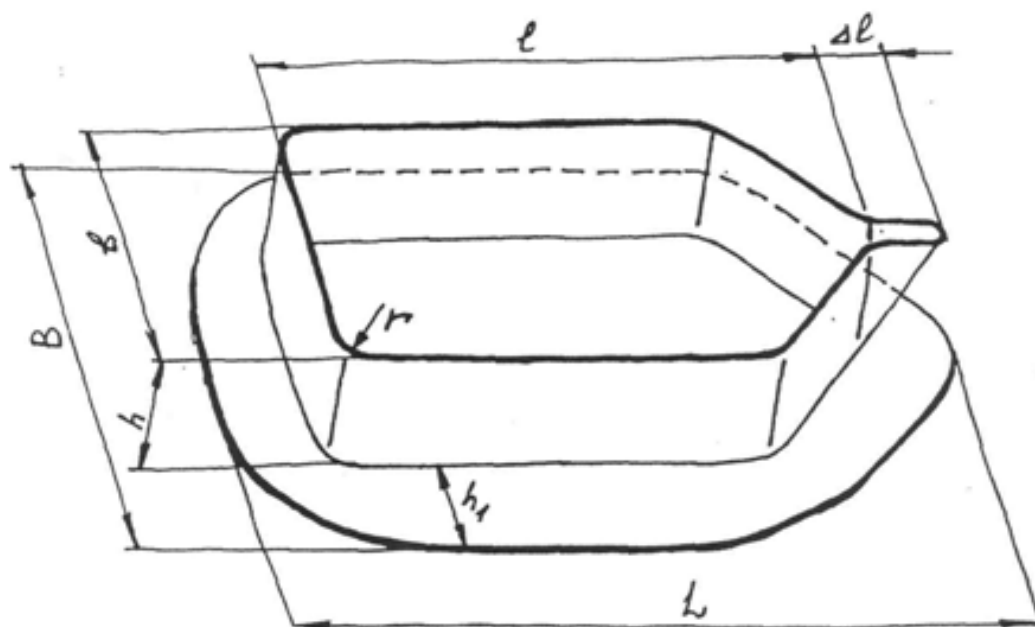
Взаимное расположение контейнера и плоской листовой заготовки
